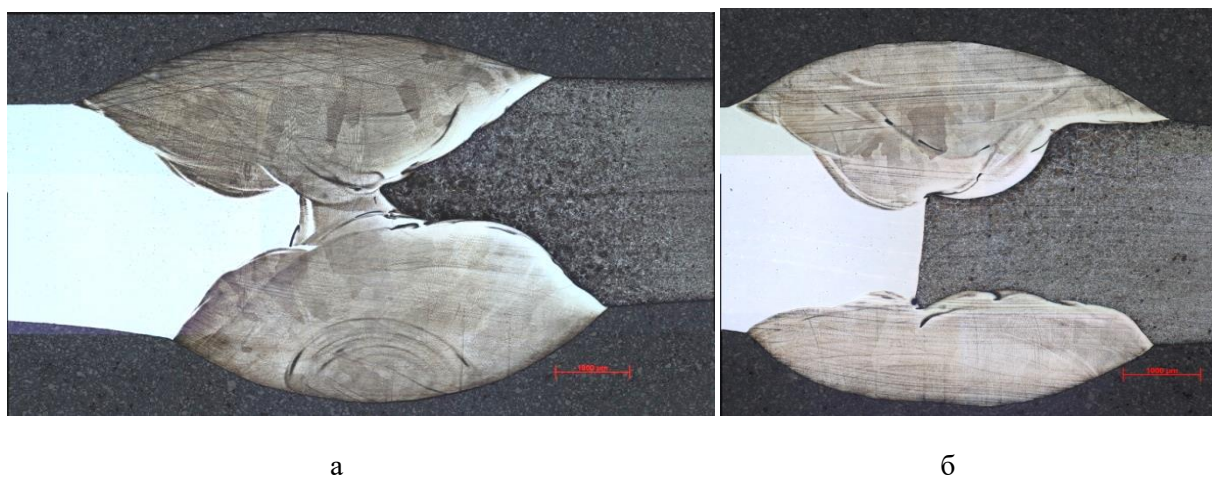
Комбинированные сварные соединения сталей 09Г2С и 12Х18Н10Т: а – соединение с полным проплавлением, без дефектов; б – сварное соединение с непроваром
